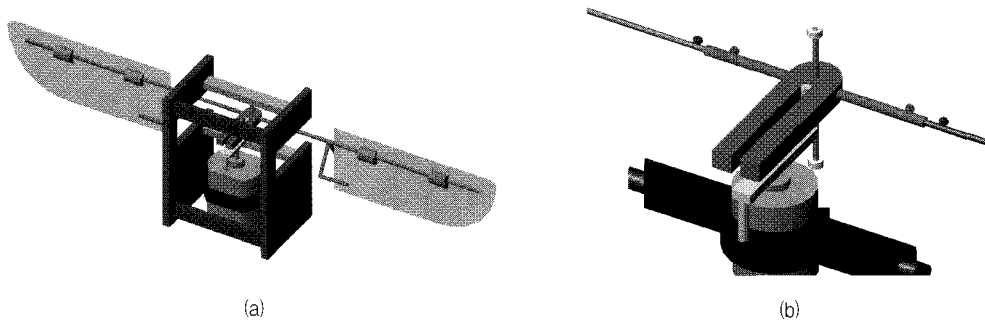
Motor-crank actuator 구조<sup>9)</sup> : (a) Motor-crank actuator and (b) Crank-link 구조
